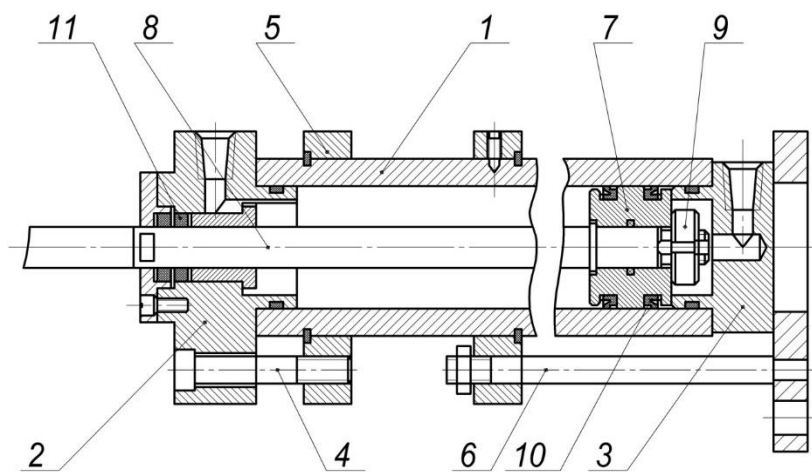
Конструктивна схема розробленого пневмоприводного циліндра для захватного пристрою
